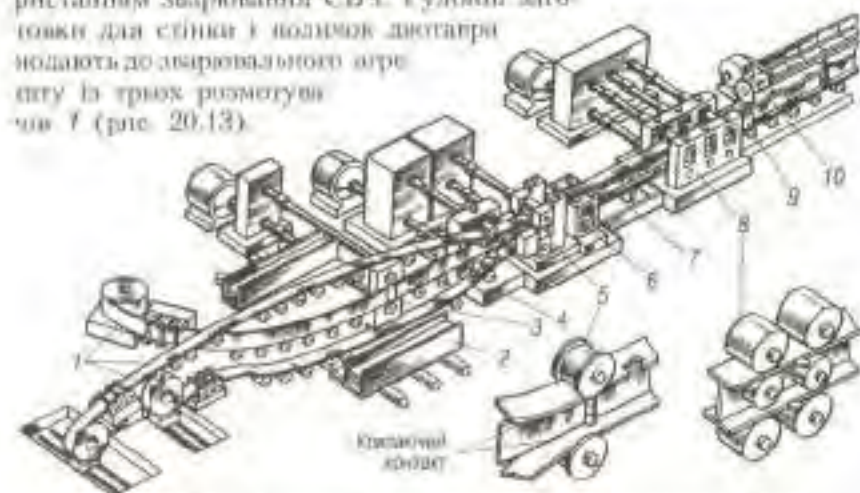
Схема агрегату для виготовлення двотаврових профілів зварюванням СВЧ
